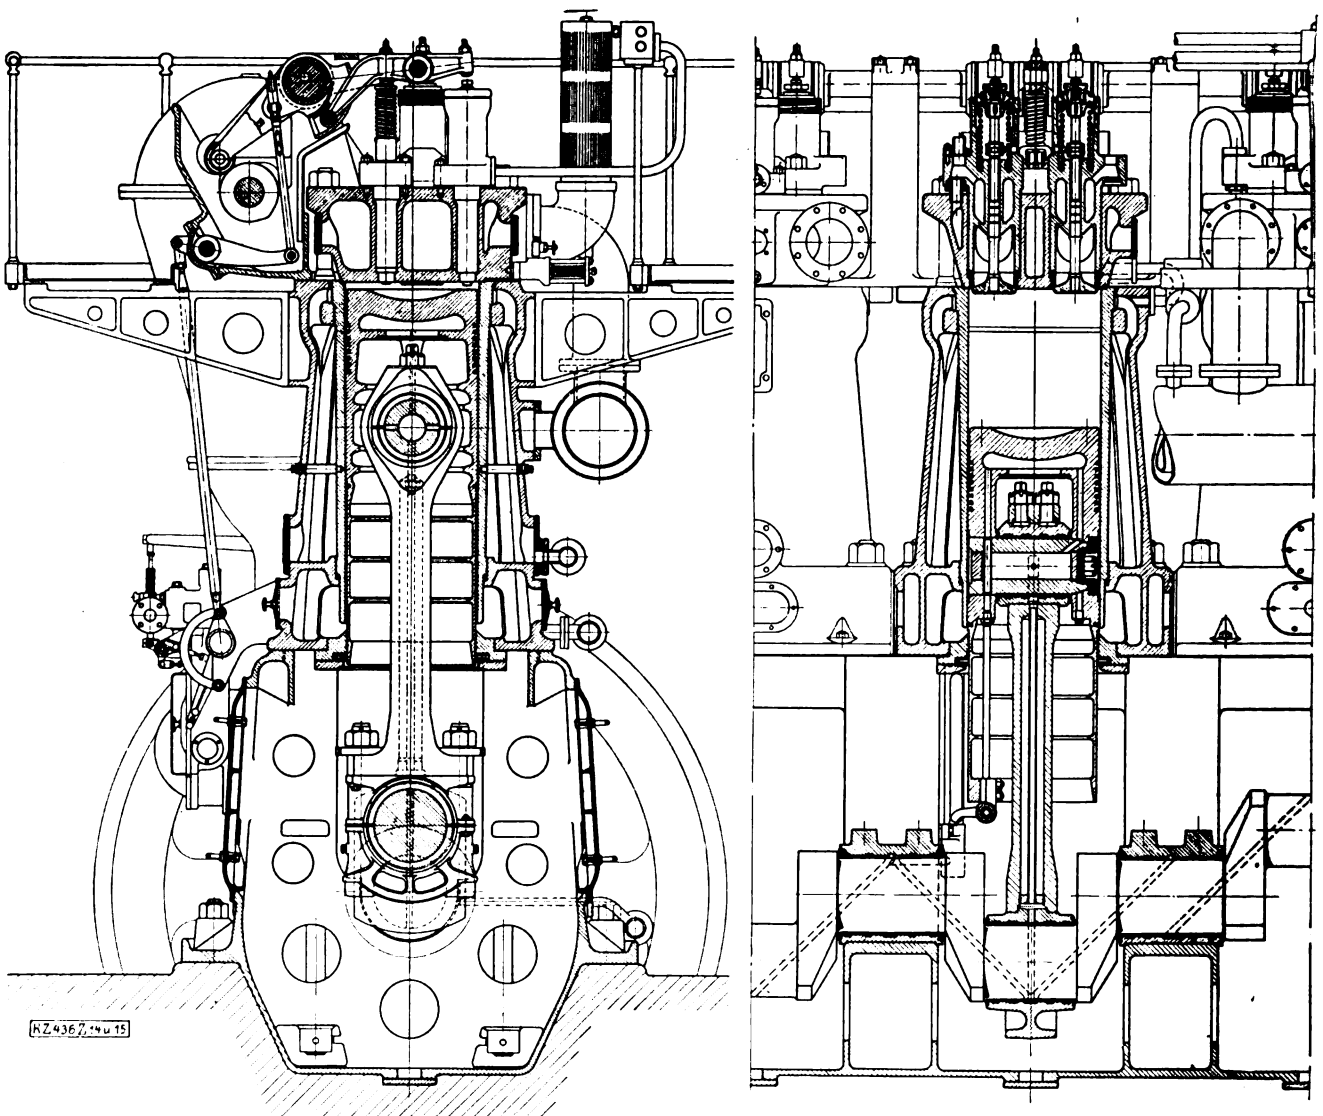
und 15. Senkrechte Hauptschnitte der Sechszylinder-Dieselmachine von 1140 PS_e der Snow Holly Works.
